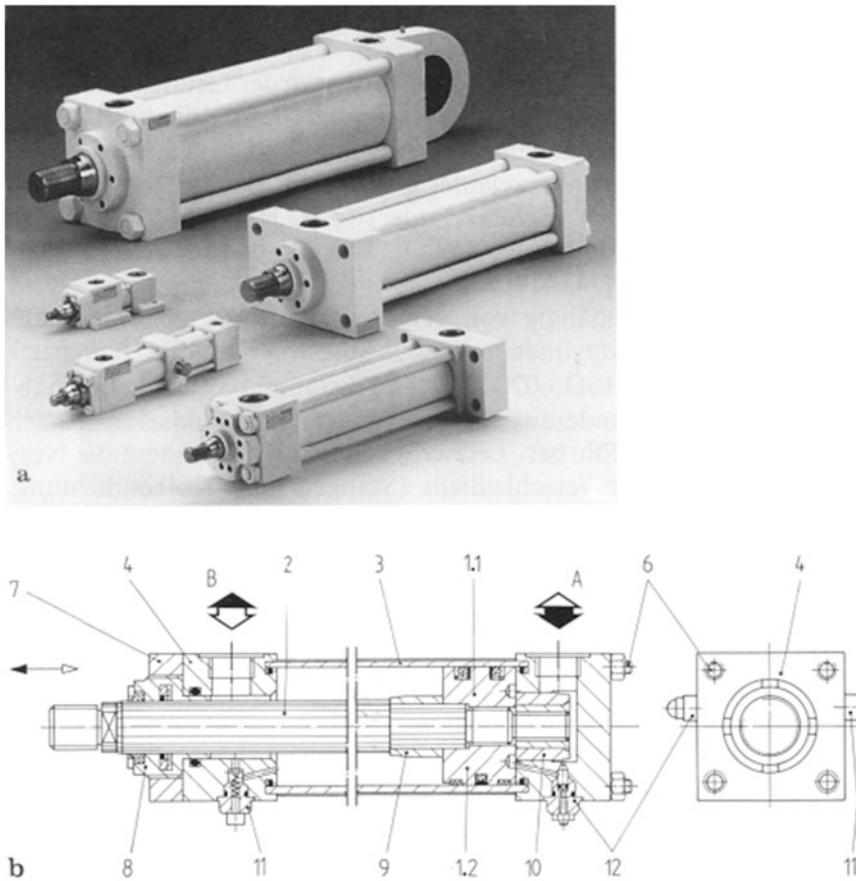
Differenzialzylinder in Zugankerbauform (DIN 24554, DIN ISO 6020 Teil 2; CD 160, Bosch Rexroth). a In Varianten nach Baugröße und Befestigungsart; b mit rechteckigem Flansch am Zylinderkopf. 1.1 Kolben mit Lippenring-(Nutring und Stützring-) Kolbendichtung für leckarmen Betrieb, 1.2 mit Gleitring-(gummivorgespannter Kunststoff-) Kolbendichtung für reibungsarmen Betrieb, 2 Kolbenstange, 3 Zylinderrohr, 4 Zylinderkopf, 5 Zylinderboden, 6 Zuganker, 7 rechteckiger Flansch, 8 Lagermetall-Führungsbuchse mit Stangendichtung und Abstreifer, 9 Dämpferkolben mit Buchse, 10 Dämpferzapfen mit Buchse, 11 Rückschlag-Einbauventil mit Entlüftung, 12 Drossel-Einbauventil einstellbar
